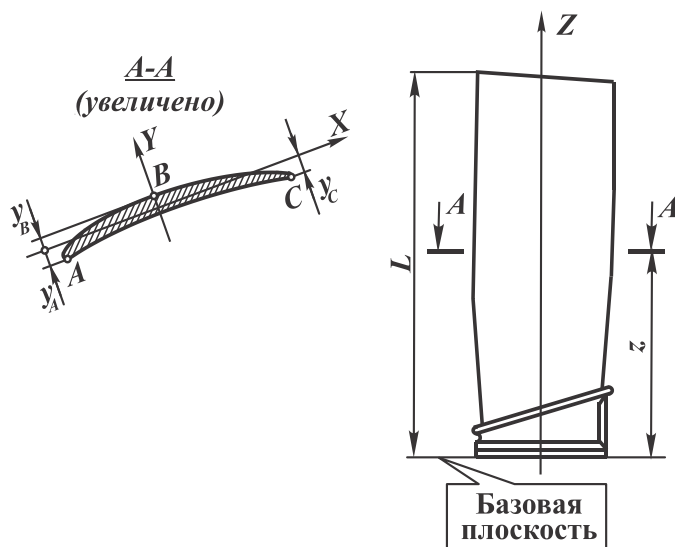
Лопатка 3-й ступени компрессора ГТД ТВ3-117
